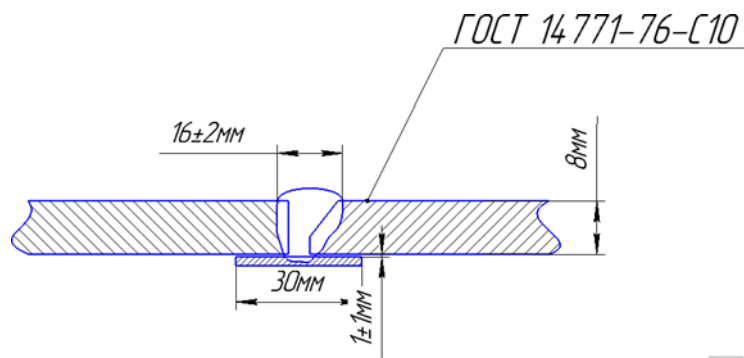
Вид сварного шва сварки краёв днища между собой
